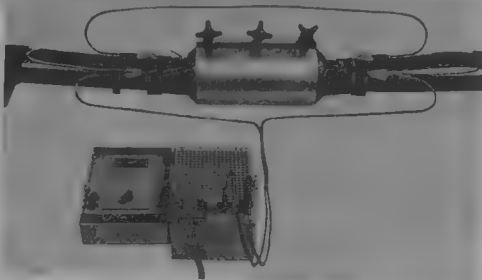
Gleichzeitiges Schweißen von 4 PE-Kabelenden in einer Abzweigmuffe.
